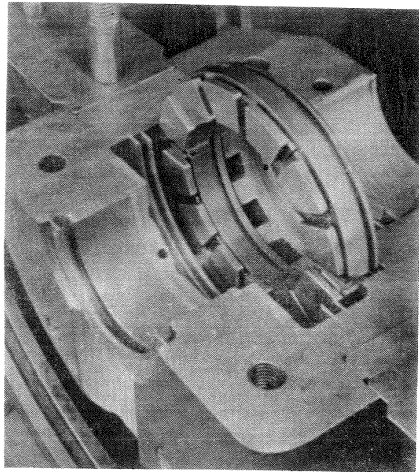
Cojinete de empuje para eje horizontal.
